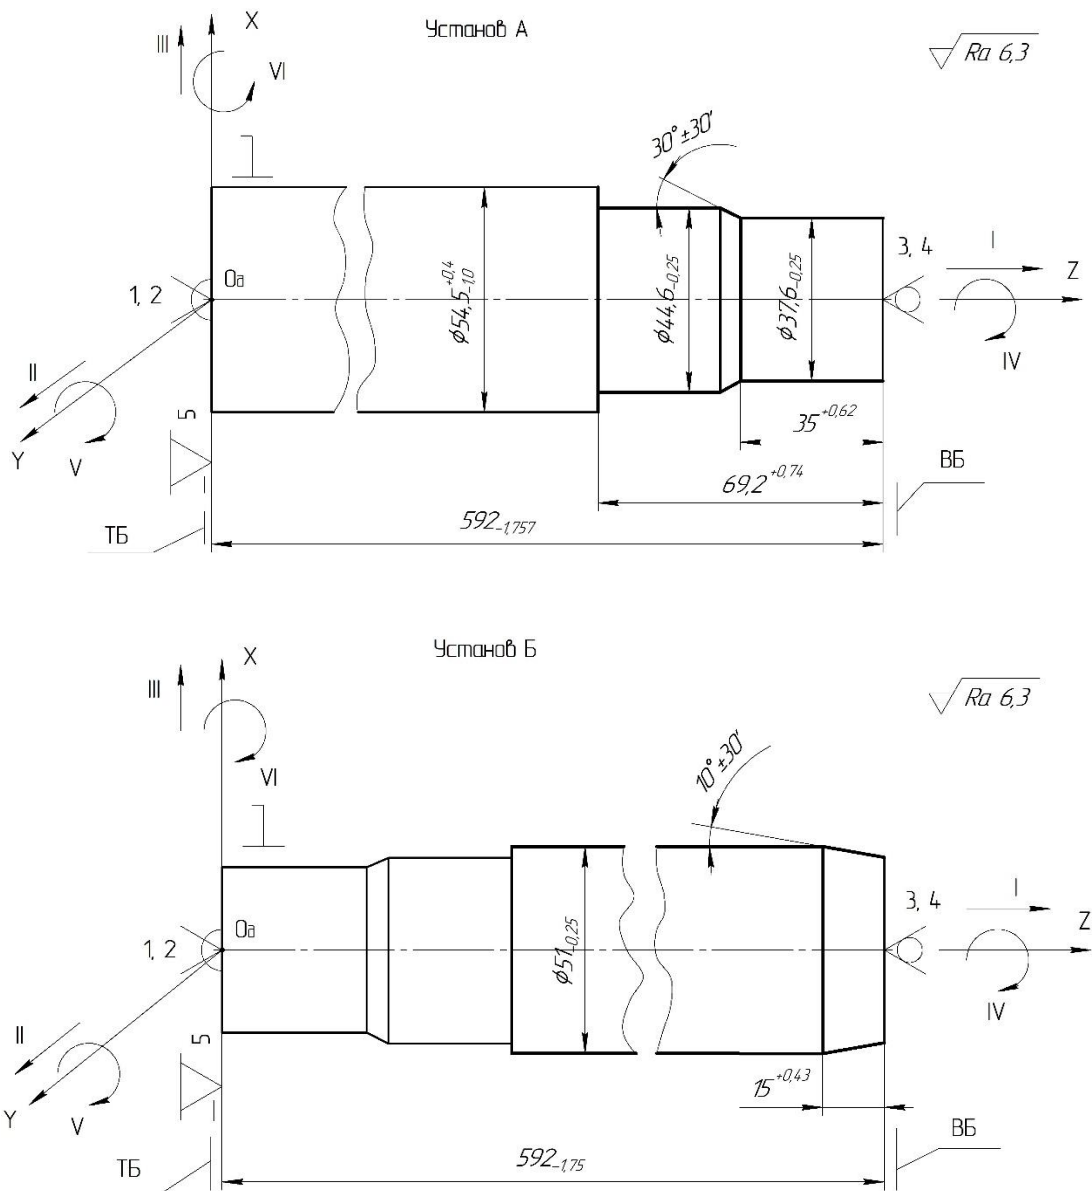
Ескізи заготовки на операції 015 (установи А і Б). Схема № 1
